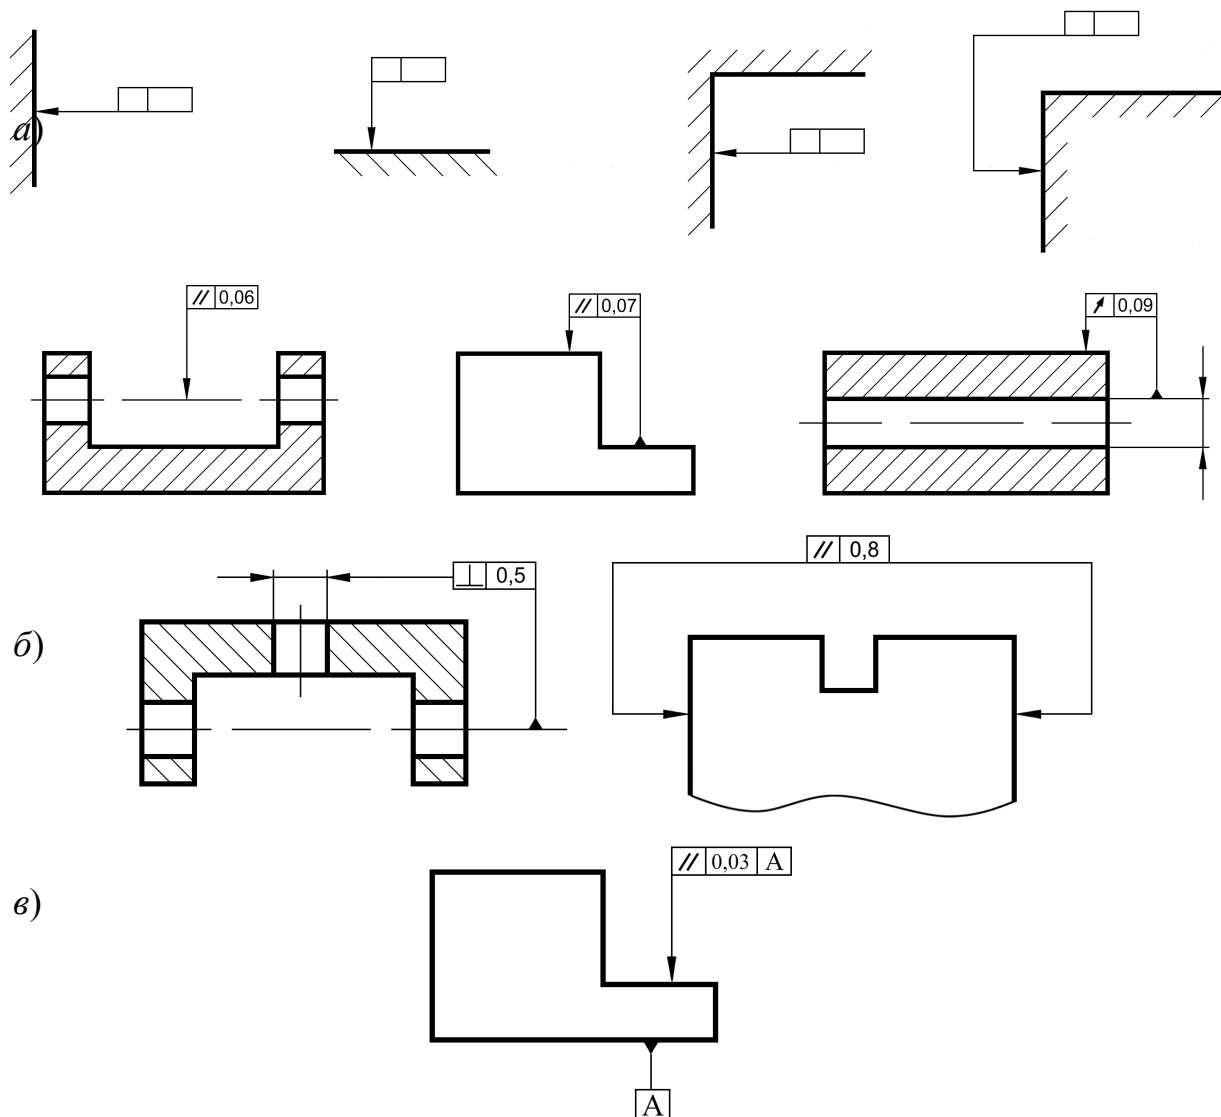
Примеры условных обозначений допусков формы и расположения поверхностей
